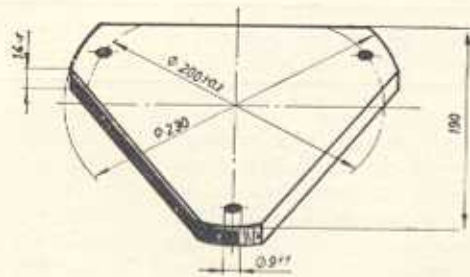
Vorrichtung zum Entspannen und Einstellen der Kupplung (Maßskizze)
